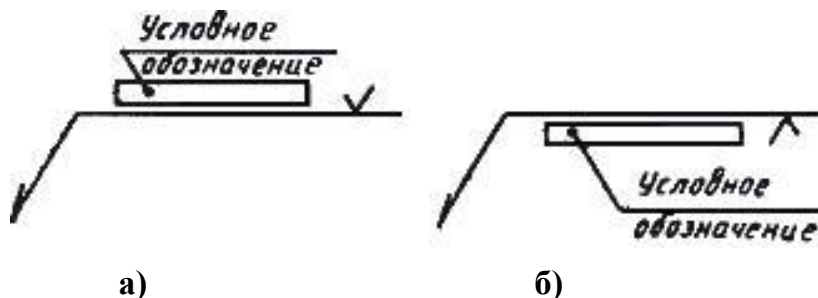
Обозначение нестандартного шва [5]: а – с лицевой стороны; б – с оборотной стороны
